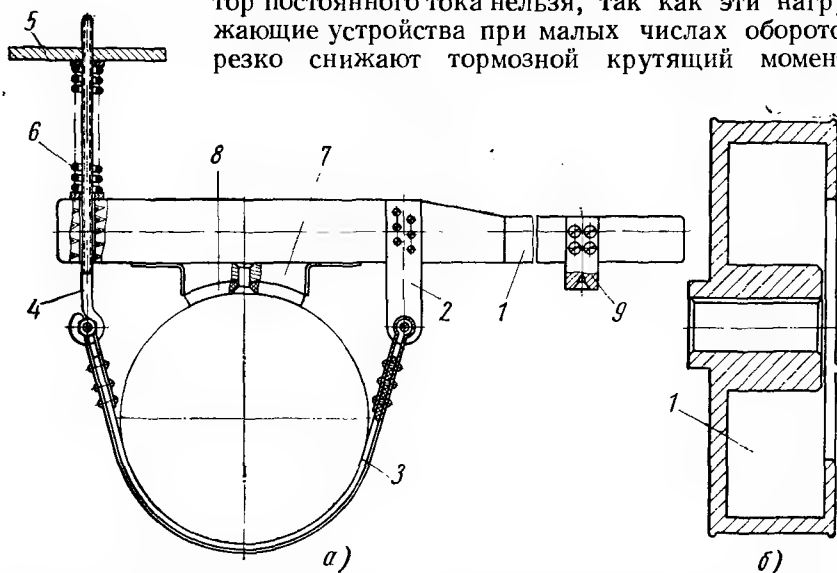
Колодочно-ленточный тормоз (а) и шкив (б) для нагружения пластинчатых гидромоторов
